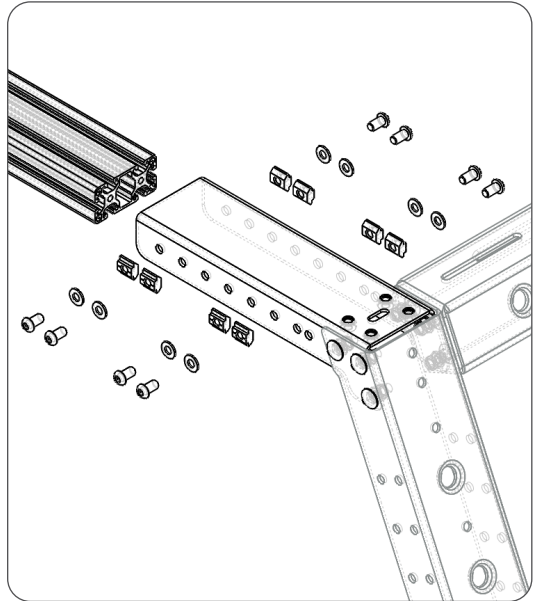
Detailansicht der verschraubten Dachstrebe / detailed view of bolted down roof strut
